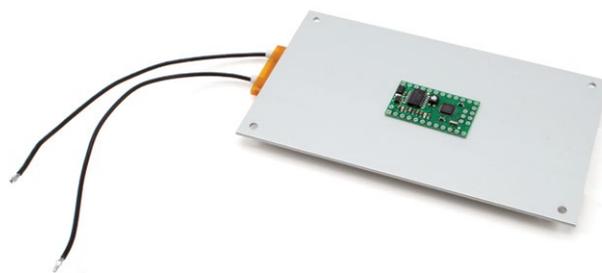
Pour le soudage, on peut placer une carte sur la plaque chauffante, après avoir enduit les pastilles de pâte à braser.
